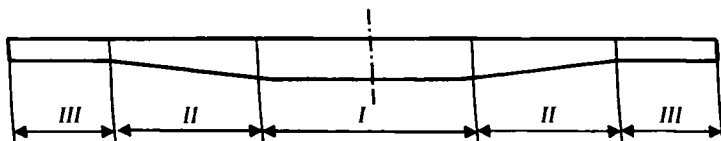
Форма профилированной заготовки малолистовой рессоры:
